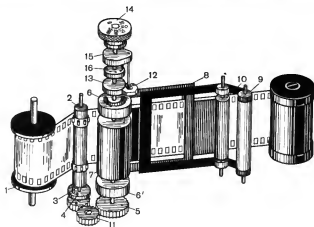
Принципиальная схема шторного затвора: 1 — приемная катушка; 2 — ось мерного валика; 3 — палец мерного валика; 4 — зуб; 5 — зубчатое колесо; 6 и 6' — шкивы; 7 — барабан; 8 — шторки; 9 и 10 — гильзы; 11 — зубчатое колесо-ограничитель; 12 — тормозная защелка; 13 — диск с короткой и длинной шпильками; 14 — головка установки выдержек; 15 — диск с двумя шпильками; 16 — диск с отверстием для короткой шпильки
